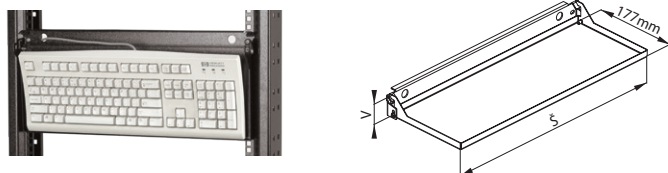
PLATEAU COULISSANT POUR CLAVIER 19" DP-PV
